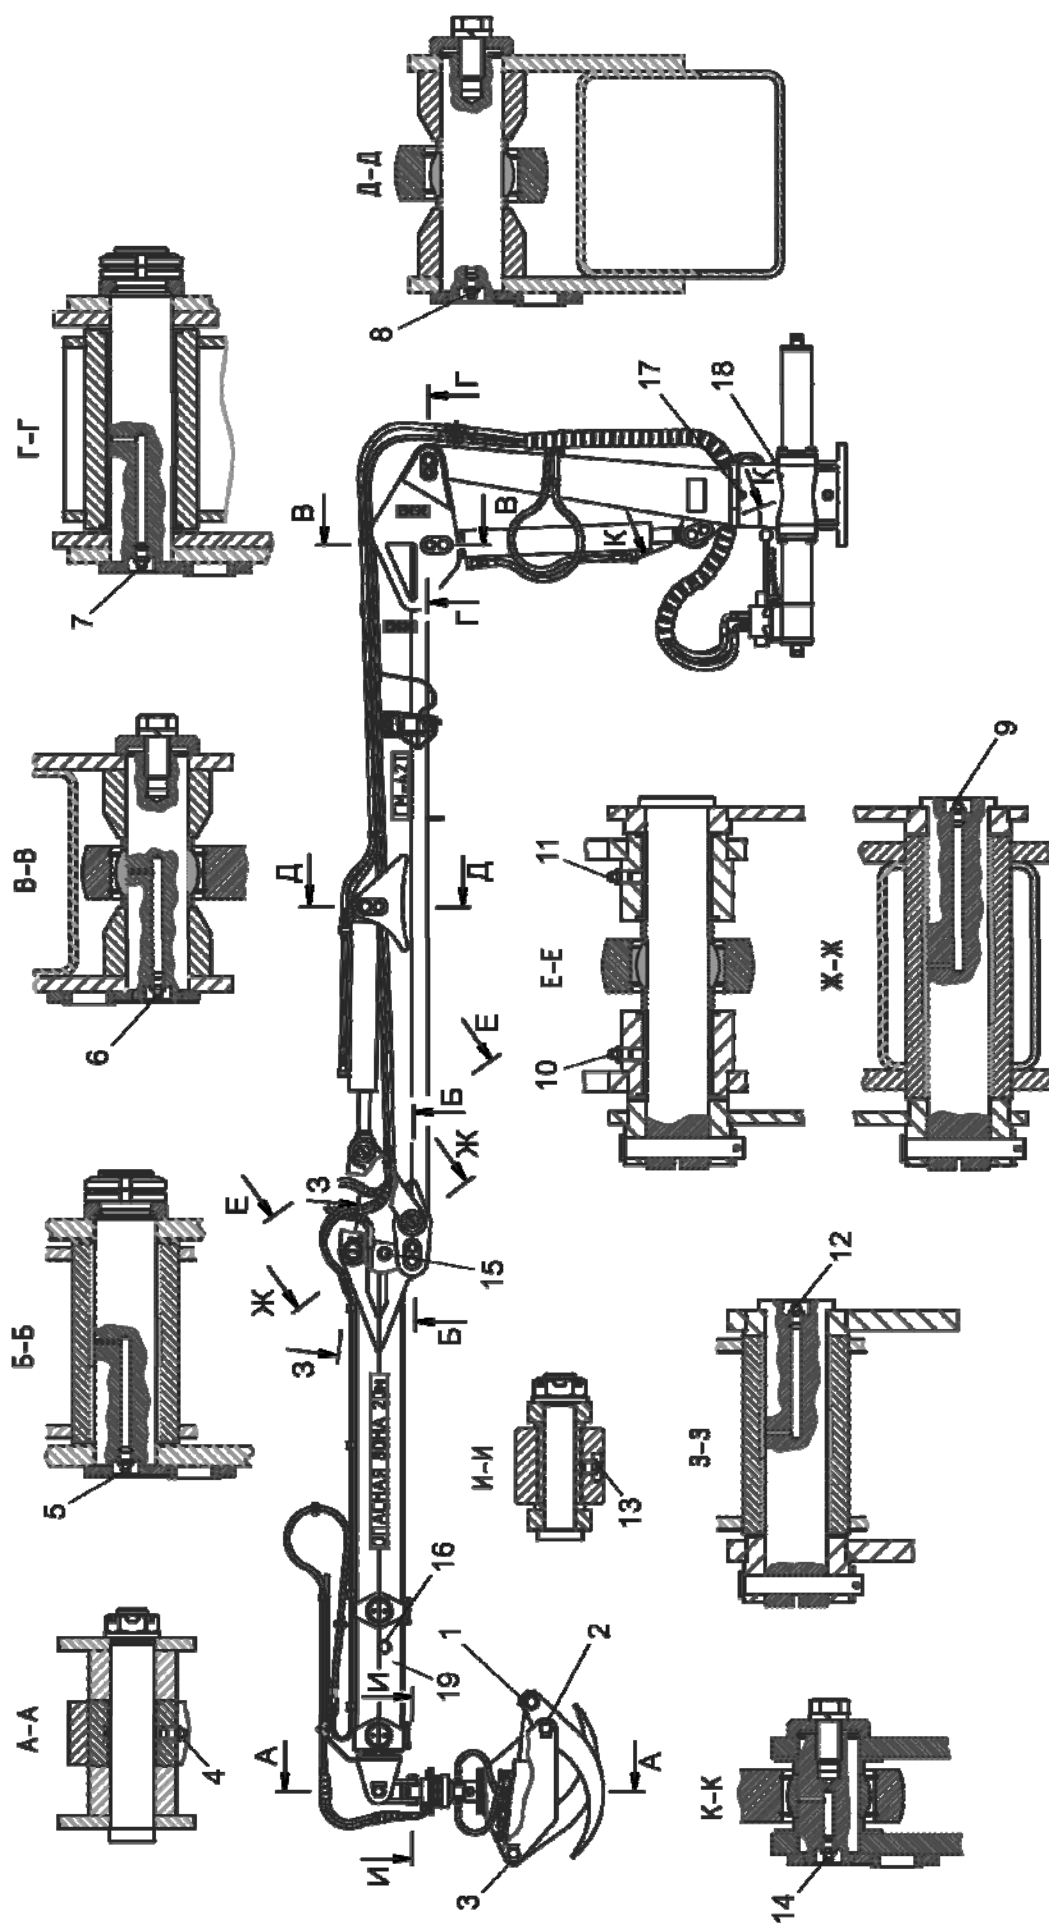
Схема смазки гидроманипулятора ГМ-42Т-01
